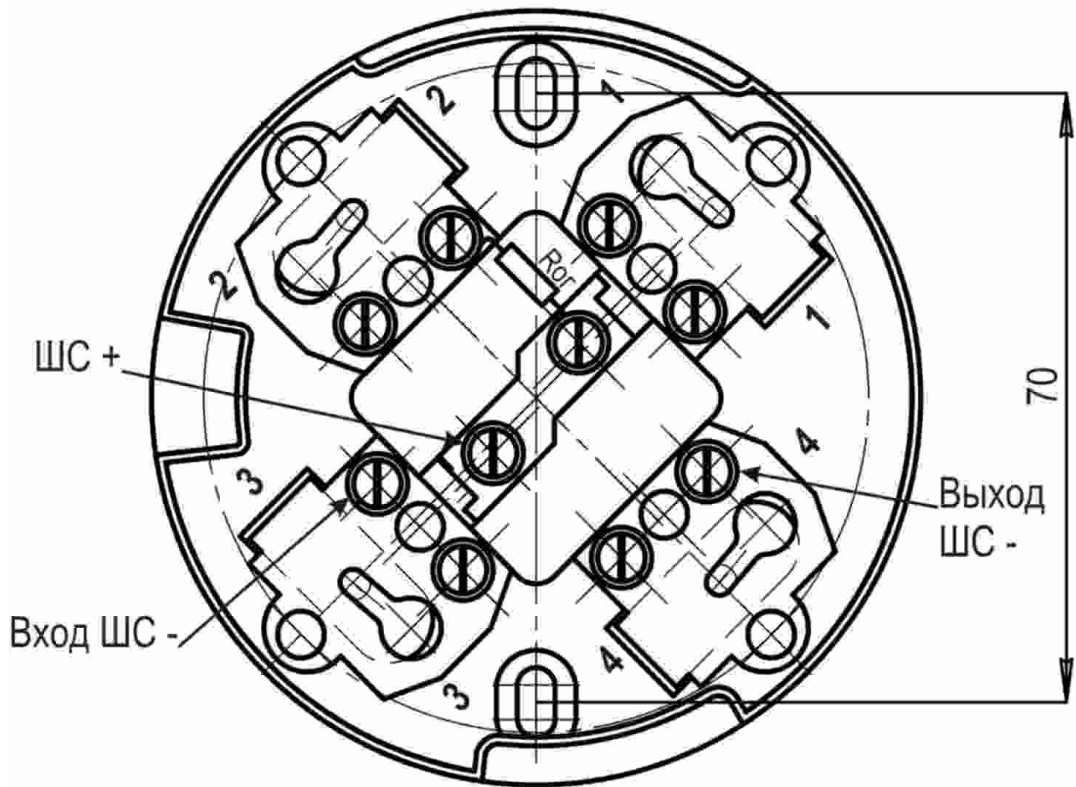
Розетка извещателя. Общий вид и расположение контактов
